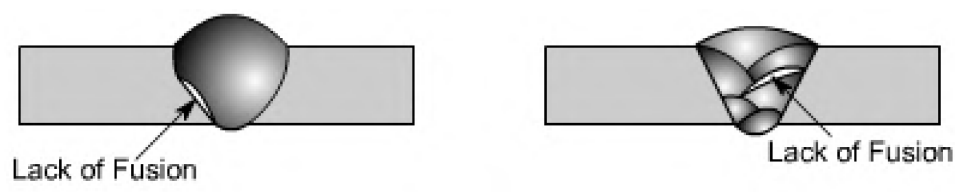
Defeito de Lack of Fusion na Solda Aluminotérmica
